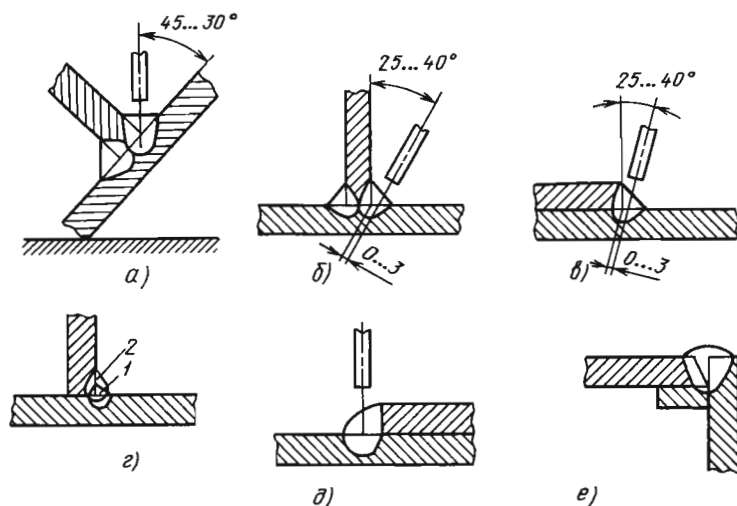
Схемы сварки угловых швов:
